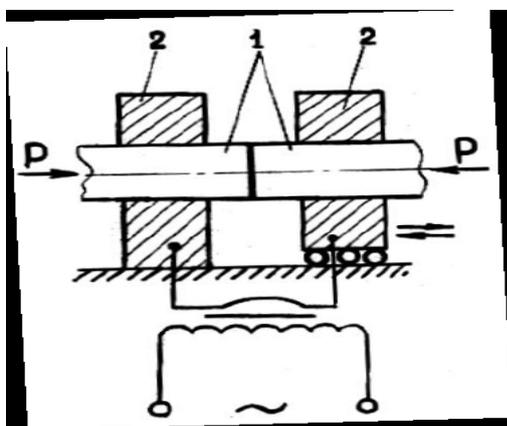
Схема стыковой контактной сварки: 1 – свариваемые заготовки; 2 – зажимы (электроды) сварочной машины
